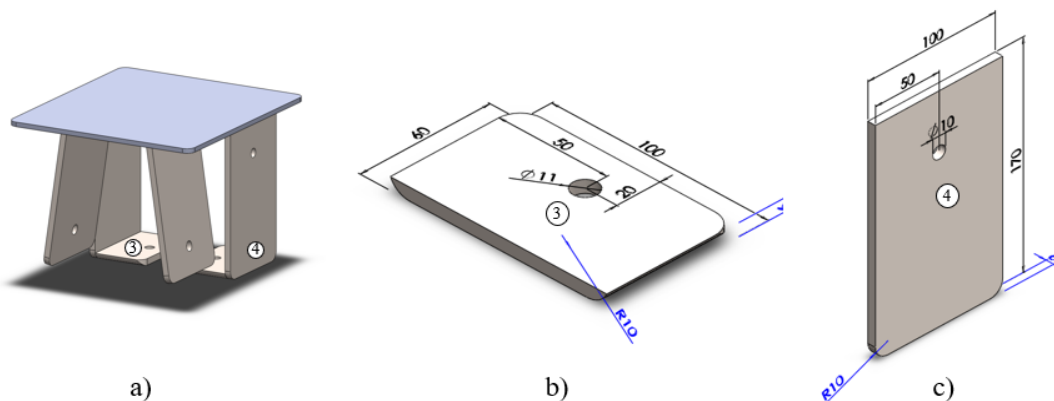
a) Subconjunto em perspetiva; b) Dimensões da Chapa Horizontal; c) Dimensões da Chapa Vertical (mm).
